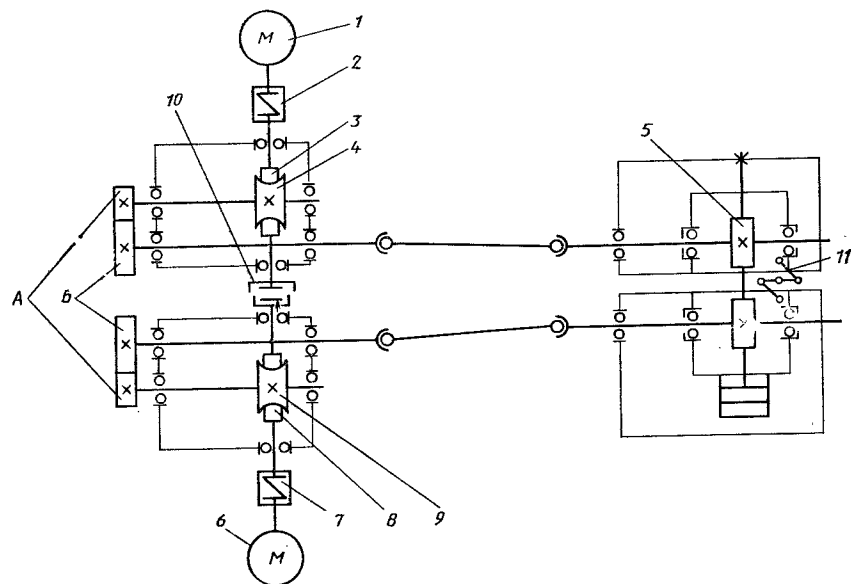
Кинематическая схема двухроликowego резьбо- и профиленкатного полуавтомата с двусторонним электроприводом
